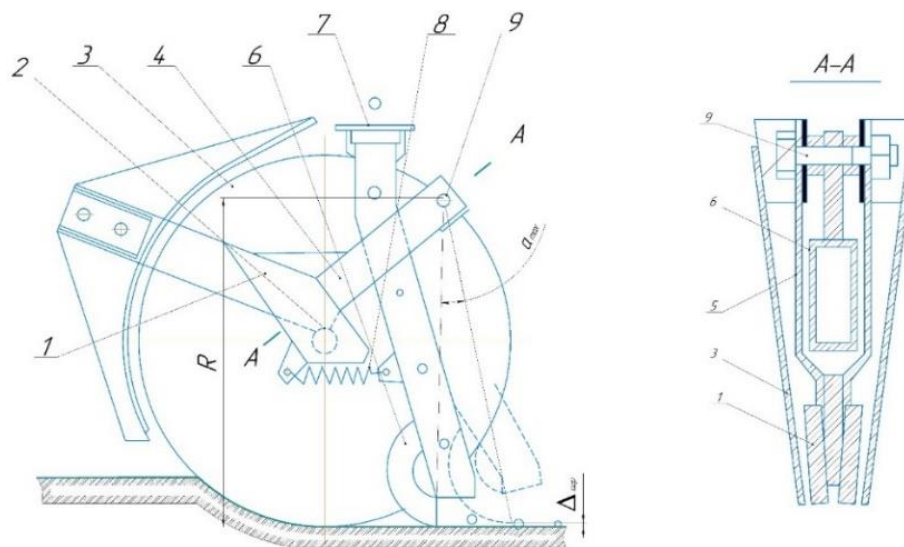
Схема дводискового комбінованого сошника: 1 – корпус; 2 – вісь; 3 – диск; 4 – тримач; 5 – щока; 6 – розтруб; 7 – наральник; 8 – пружина; 9 – шарнірна підвіска; а – вигляд збоку при знятому лівому диску, б – переріз по А-А.
